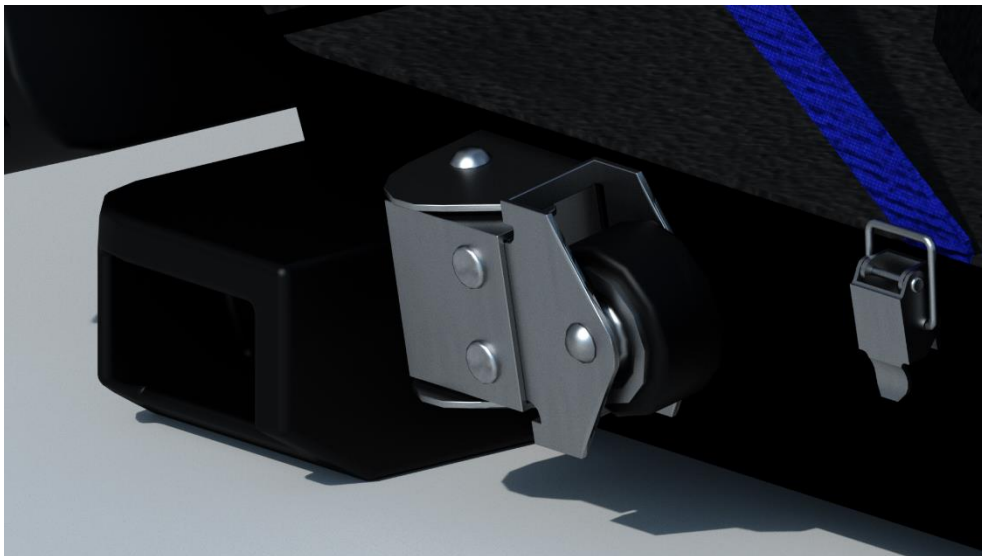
Render detalle de la rueda con mecanismo plegado
